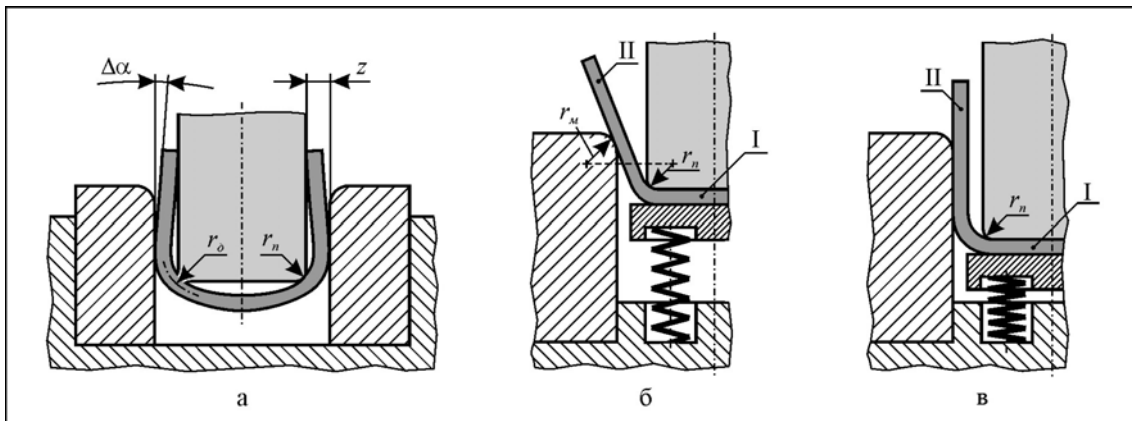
Схеми двокуттового гнуття: а – без притиску заготовки; б – з притиском заготовки (початкова стадія); в – з притиском заготовки (кінцева стадія)
